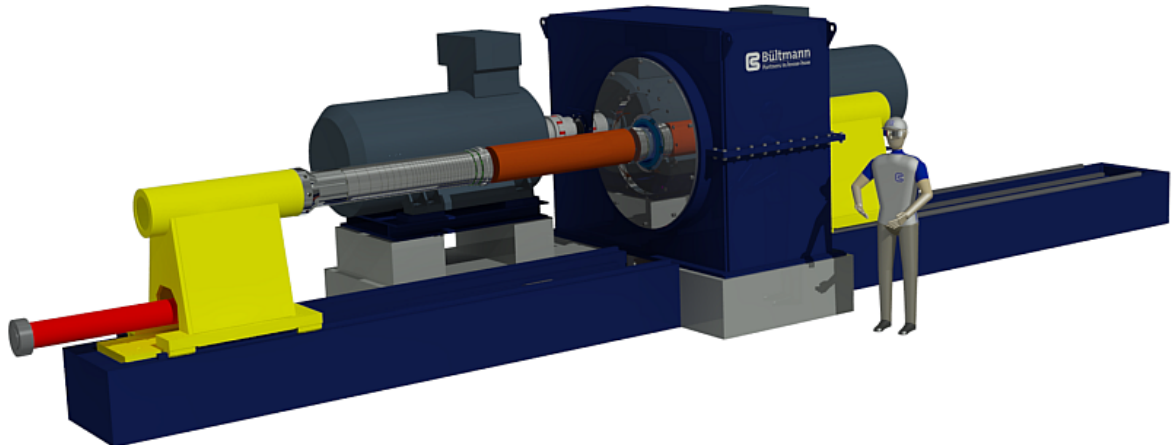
Dauermagnetheizer mit Bolzen in Bolzenwechselform mit Spannschlitten (gelb), Hybridwellen (grau) und Spannzylinder (rot) sowie Bolzen (dunkelrot)
